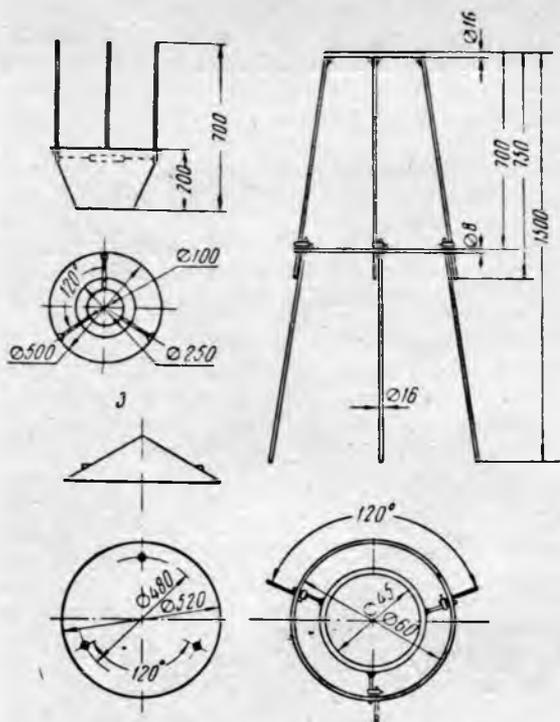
Схема устройства ловушки конструкции Б. Г. Коврова: 1 — корпус-колпак; 2 — тренога; 3 — крышка.
